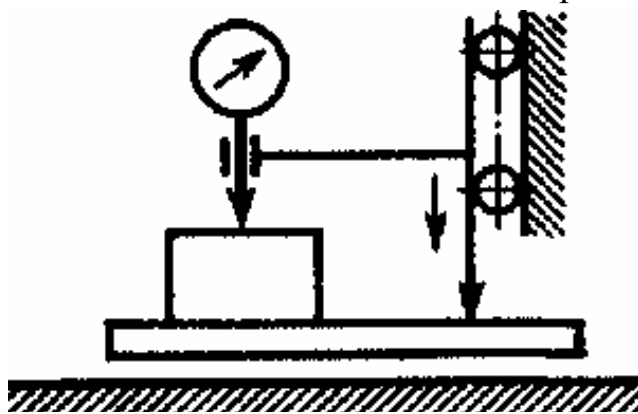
Схема компенсації нестабільної бази обробки заготовки
